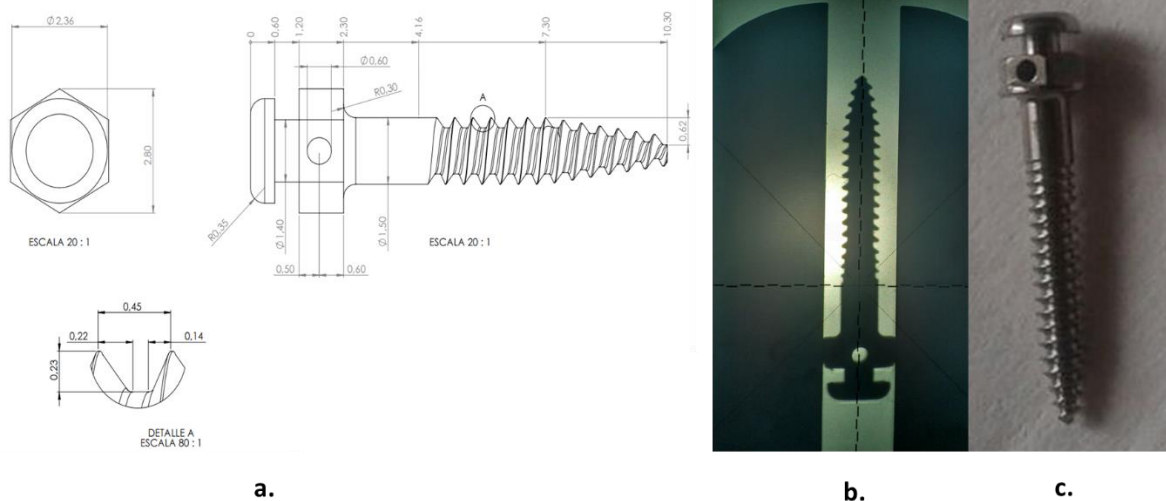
Mini-implante y sus dimensiones (unidades en mm). a. Dimensiones del mini-implante. b. Montaje en proyector de perfiles. c. mini-implante
